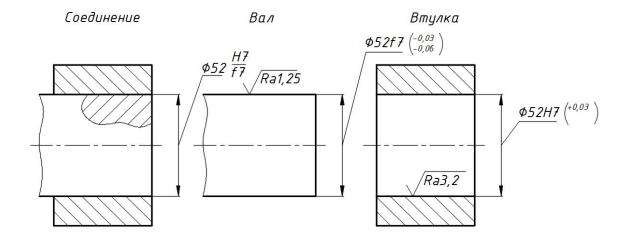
Эскизы соединения, вала и корпуса (втулки)
